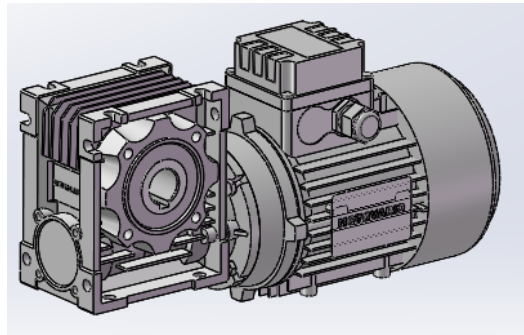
Motorreductor Motovario con reductora de tornillo sinfín.
